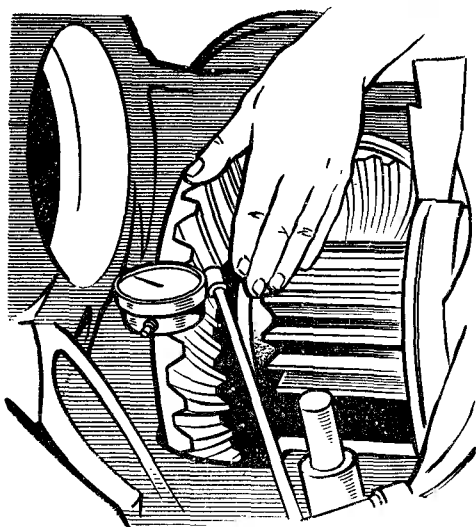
Проверка бокового зазора в зацеплении конических шестерен
